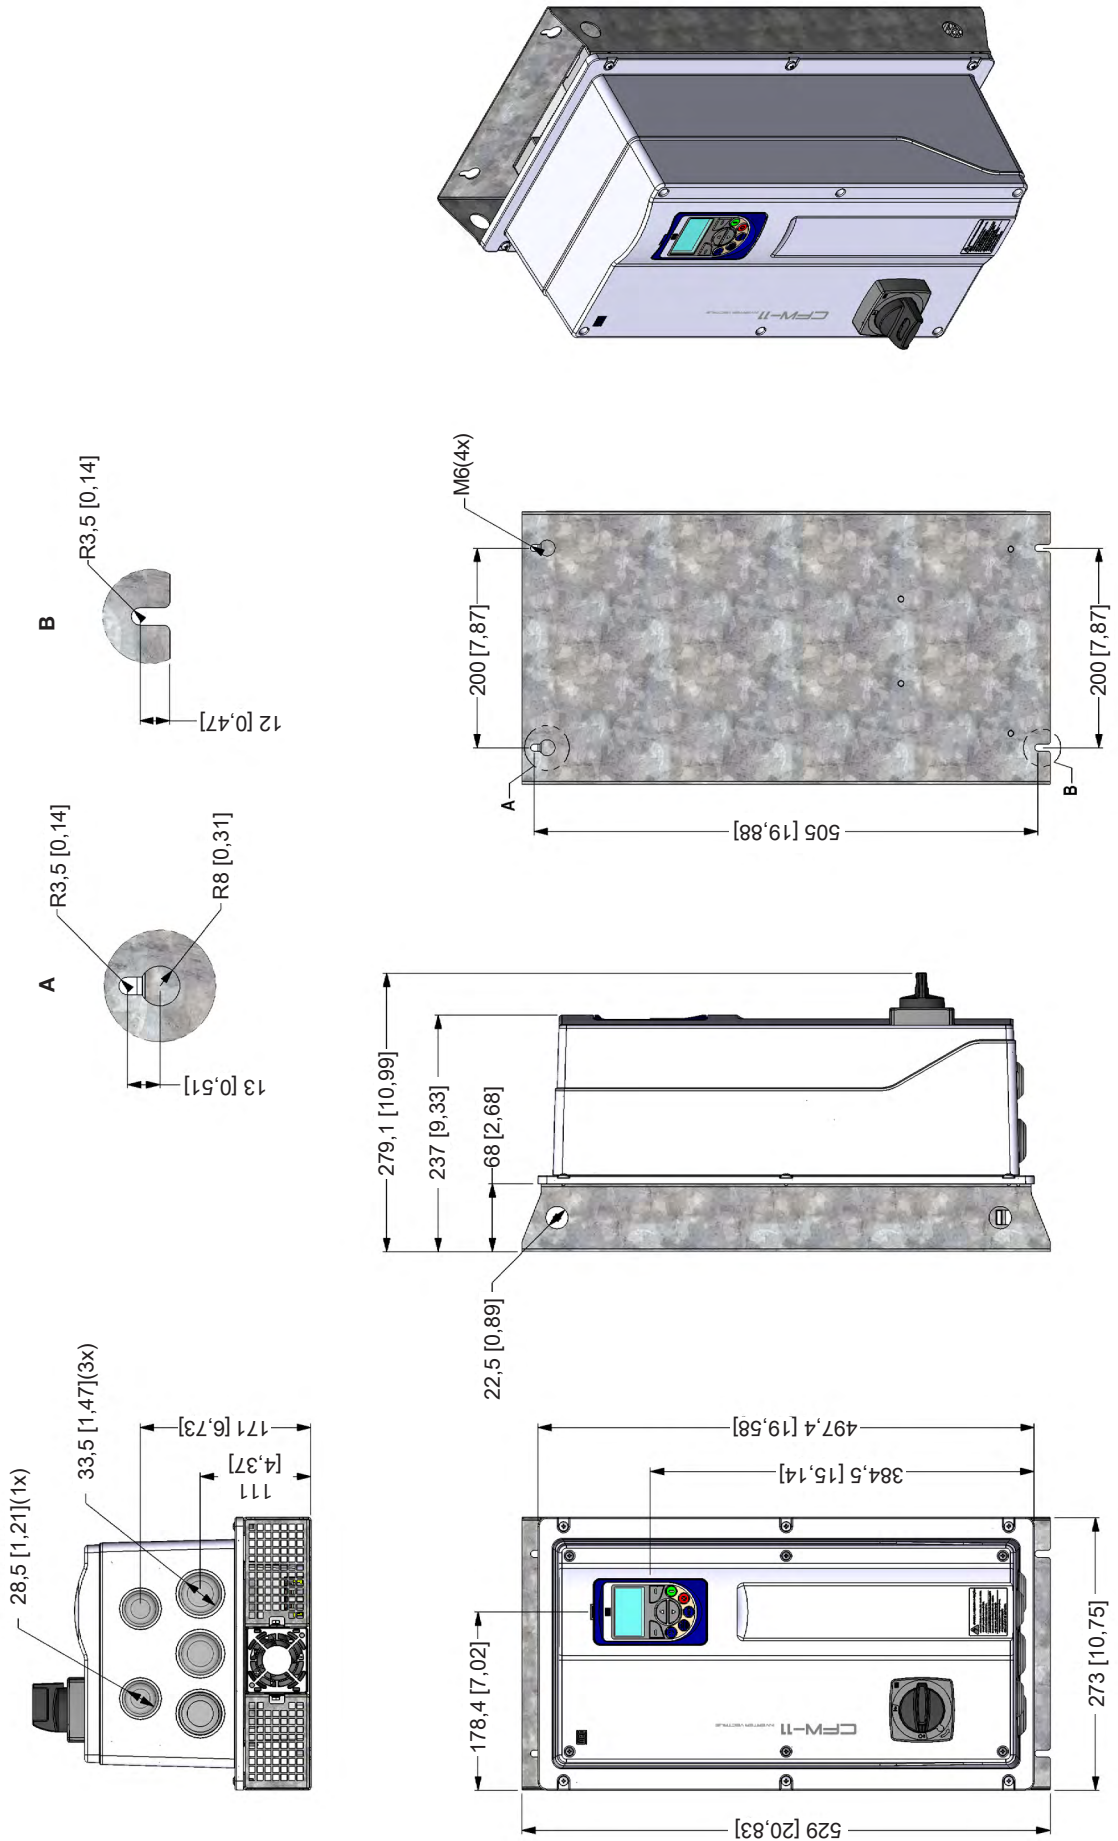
Габаритные размеры преобразователя, размер корпуса В, мм [дюйм.]
